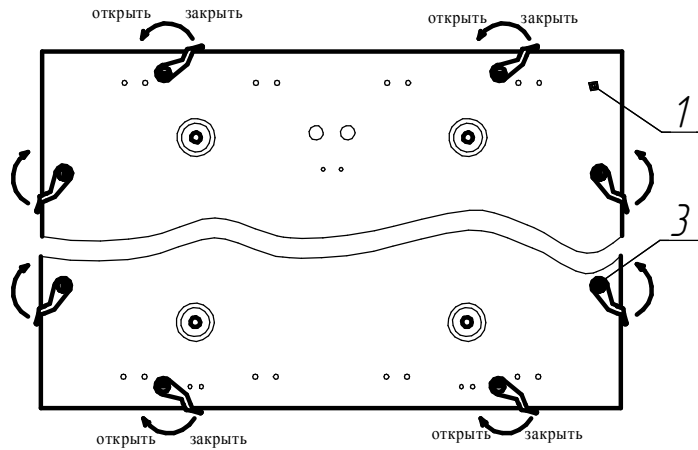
2: ЛПО46-4х18; 1. Корпус в сборе; 3. Зажим
